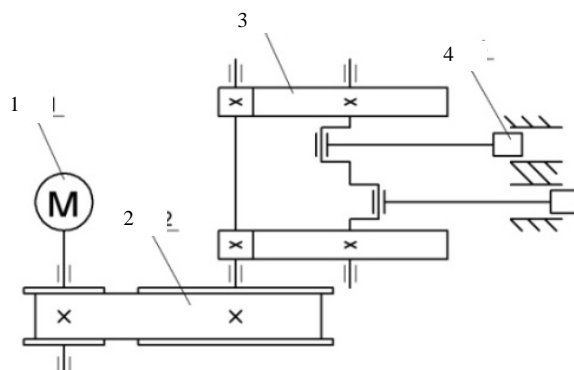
Кинематическая схема привода торфобрикетного пресса: 1 – электродвигатель; 2 – клиноременная передача; 3 – косозубая передача; 4 – кривошипно-шатунный механизм
